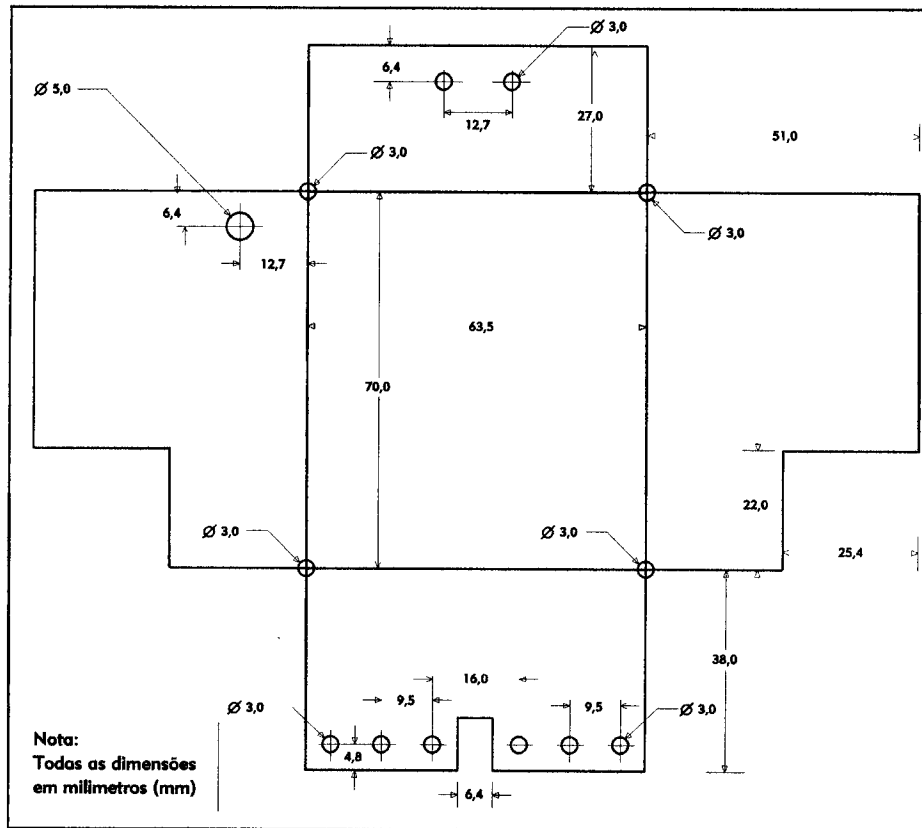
Especificações de corte e dobragem da folha de alumínio para construção da estrutura de protecção da placa de pré-amplificação.
